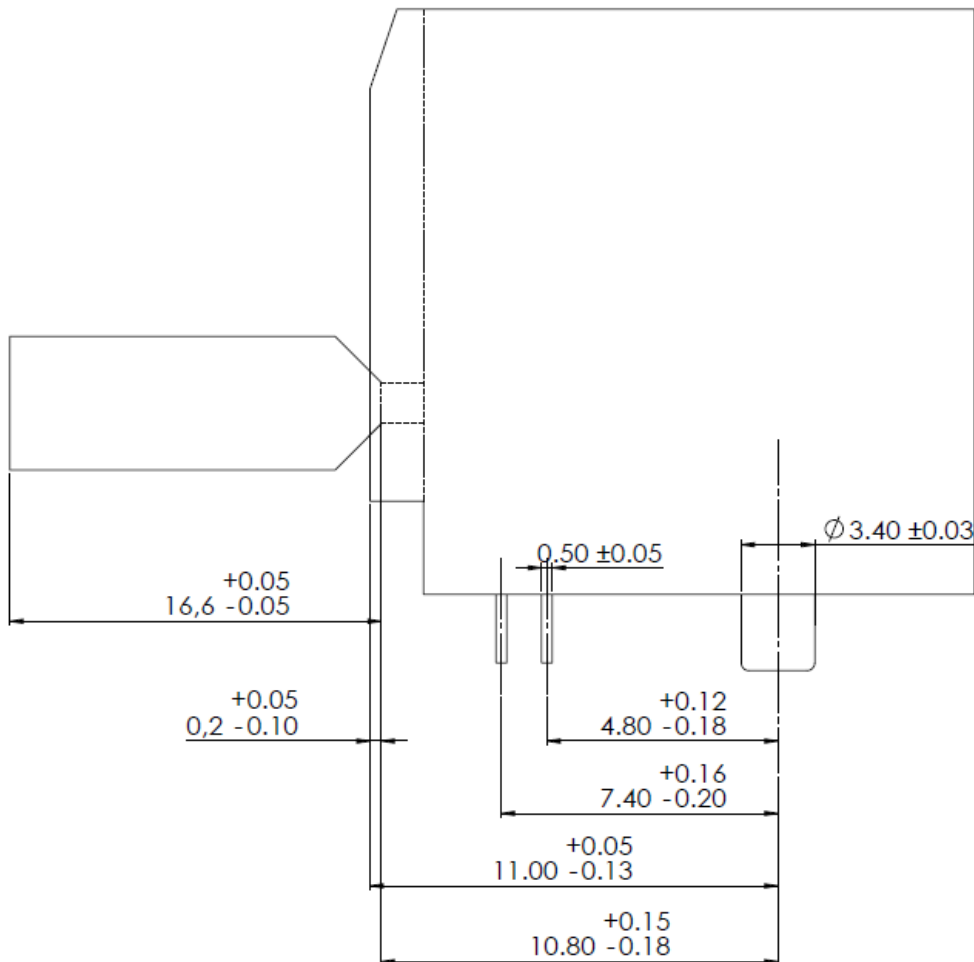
Esboço incluindo as cotas relevantes para a inserção do componente.
